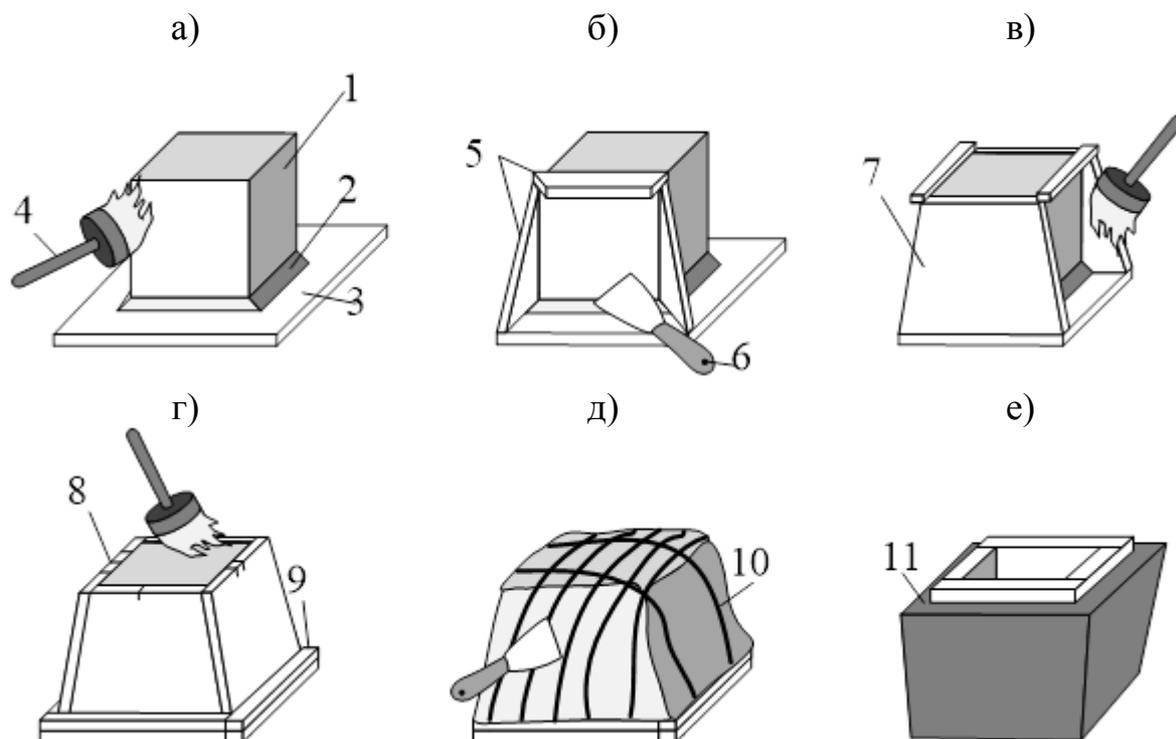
Снятие простой чистой формы с куба, состоящей из четырех кусков: а – установка модели; б – снятие торцевого куска формы; в – подготовка к отливке боковых кусков формы; г – нанесение замков, установка ограничителей и подготовка к изготовлению кожуха; д – изготовление кожуха; е – куски формы в кожухе; 1 – модель; 2 – глина или пластилин для крепления модели к щиту; 3 – щит; 4 – кисть; 5 – глиняные перегородки; 6 – шпатель или лопатка; 7 – торцевой кусок; 8 – замки; 9 – ограничители; 10 – арматура; 11 – кожух
